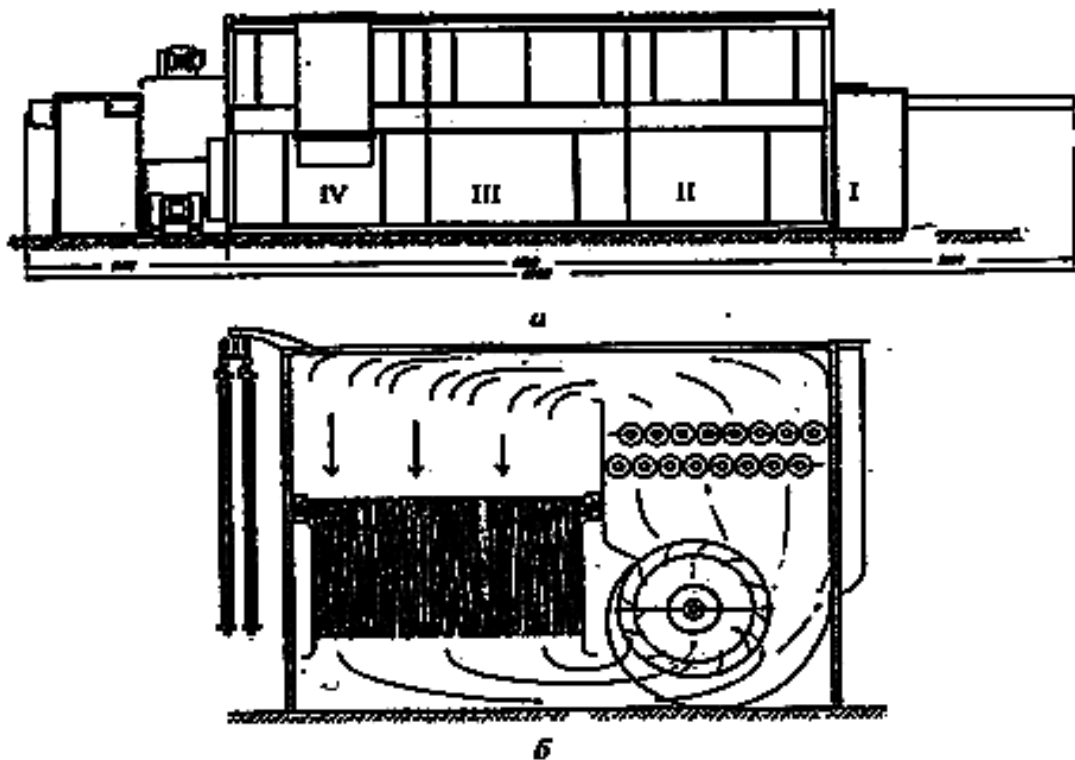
Туннельная сушилка для пряжи: а – боковой вид; б – поперечное сечение сушильной зоны с вентилятором, калорифером, несущими швялями
